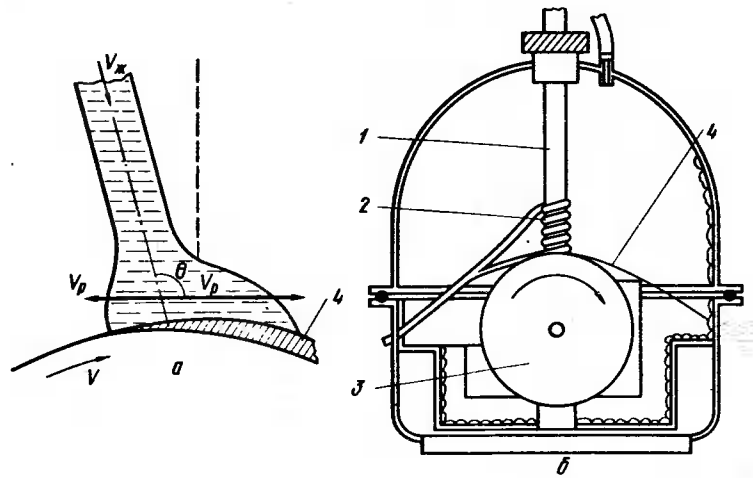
Литье струи расплава на внешнюю поверхность диска [41, 42]: а – схема формирования ленты; б – установка для литья расплава; 1 – тигель с расплавом; 2 – нагреватель; 3 – диск-холодильник; 4 – получаемая лента
